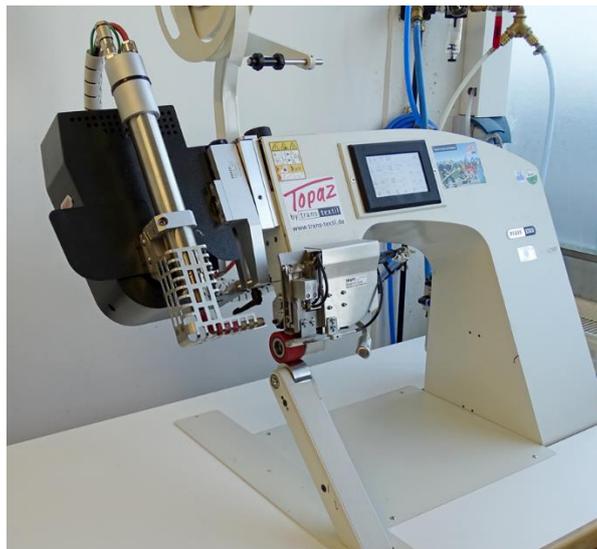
Foto der Heißluft-Schweißmaschine 8303i der Firma Pfaff Industriesysteme und Maschinen AG (Kaiserslautern) bei Fa. Trans-Textil GmbH (Freilassing).
